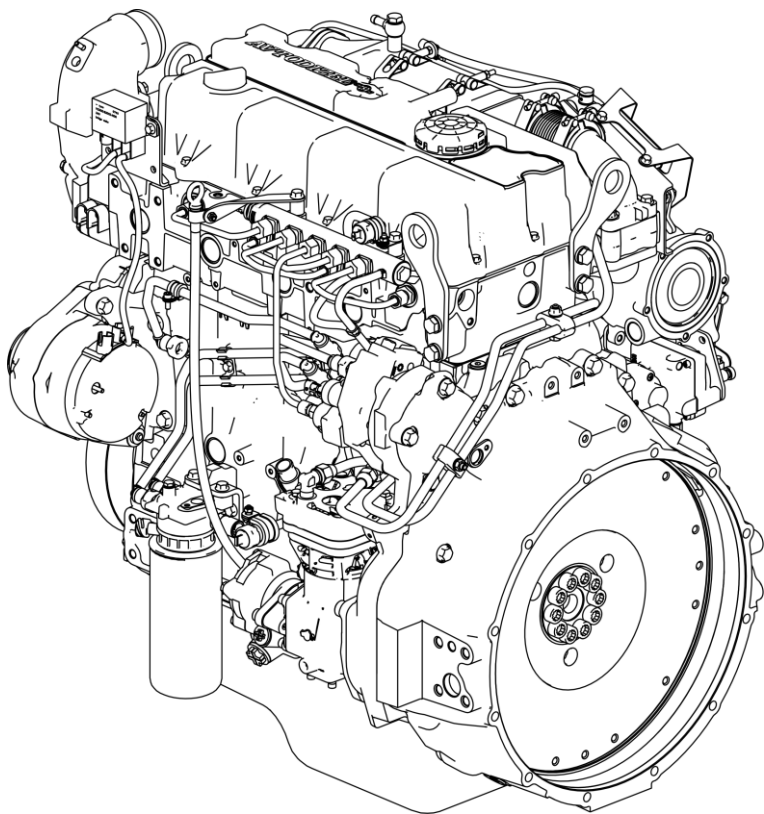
а – Двигатель ЯМЗ-53403-10 (общий вид слева)
